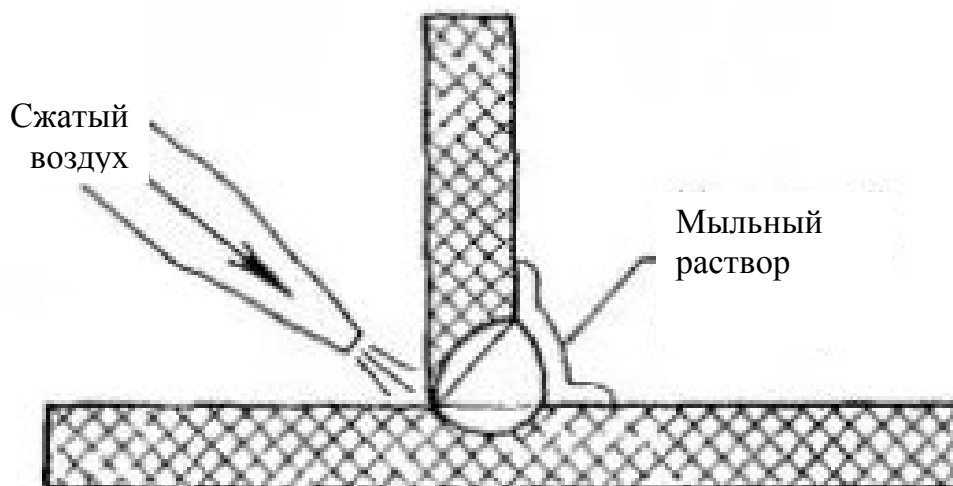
Проверка обдувом сварных соединений воздухом
